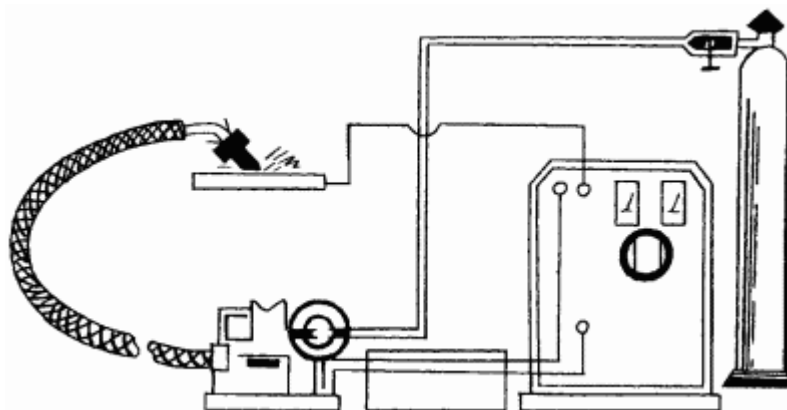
Схема сварочного полуавтомата для сварки в среде защитного газа.
